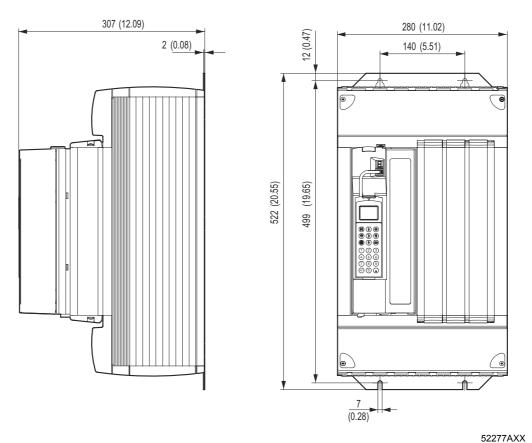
Dimensões MDX61B, tamanho 4, dimensões em mm (in)
